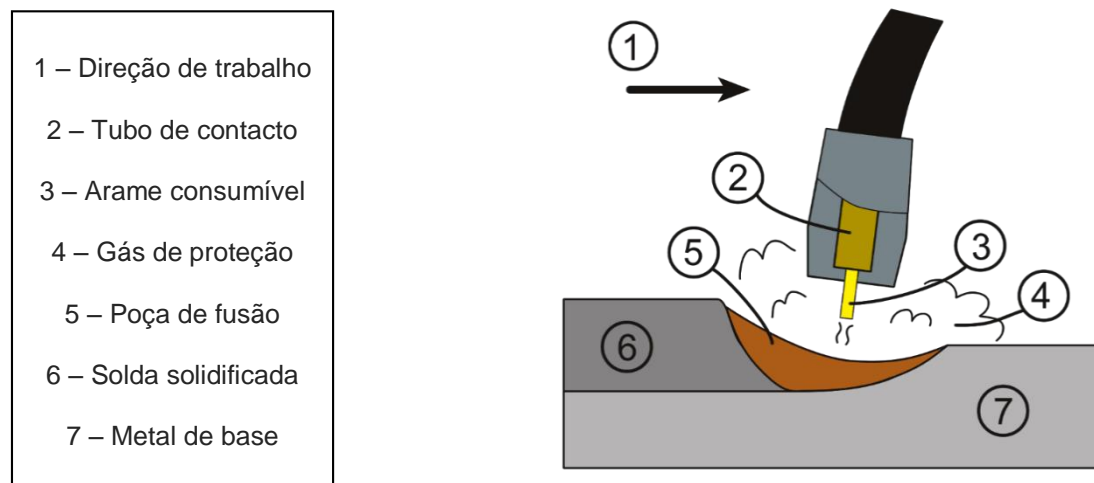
Representação esquemática do processo de soldadura MIG/MAG (fonte: commons.wikimedia.org).
